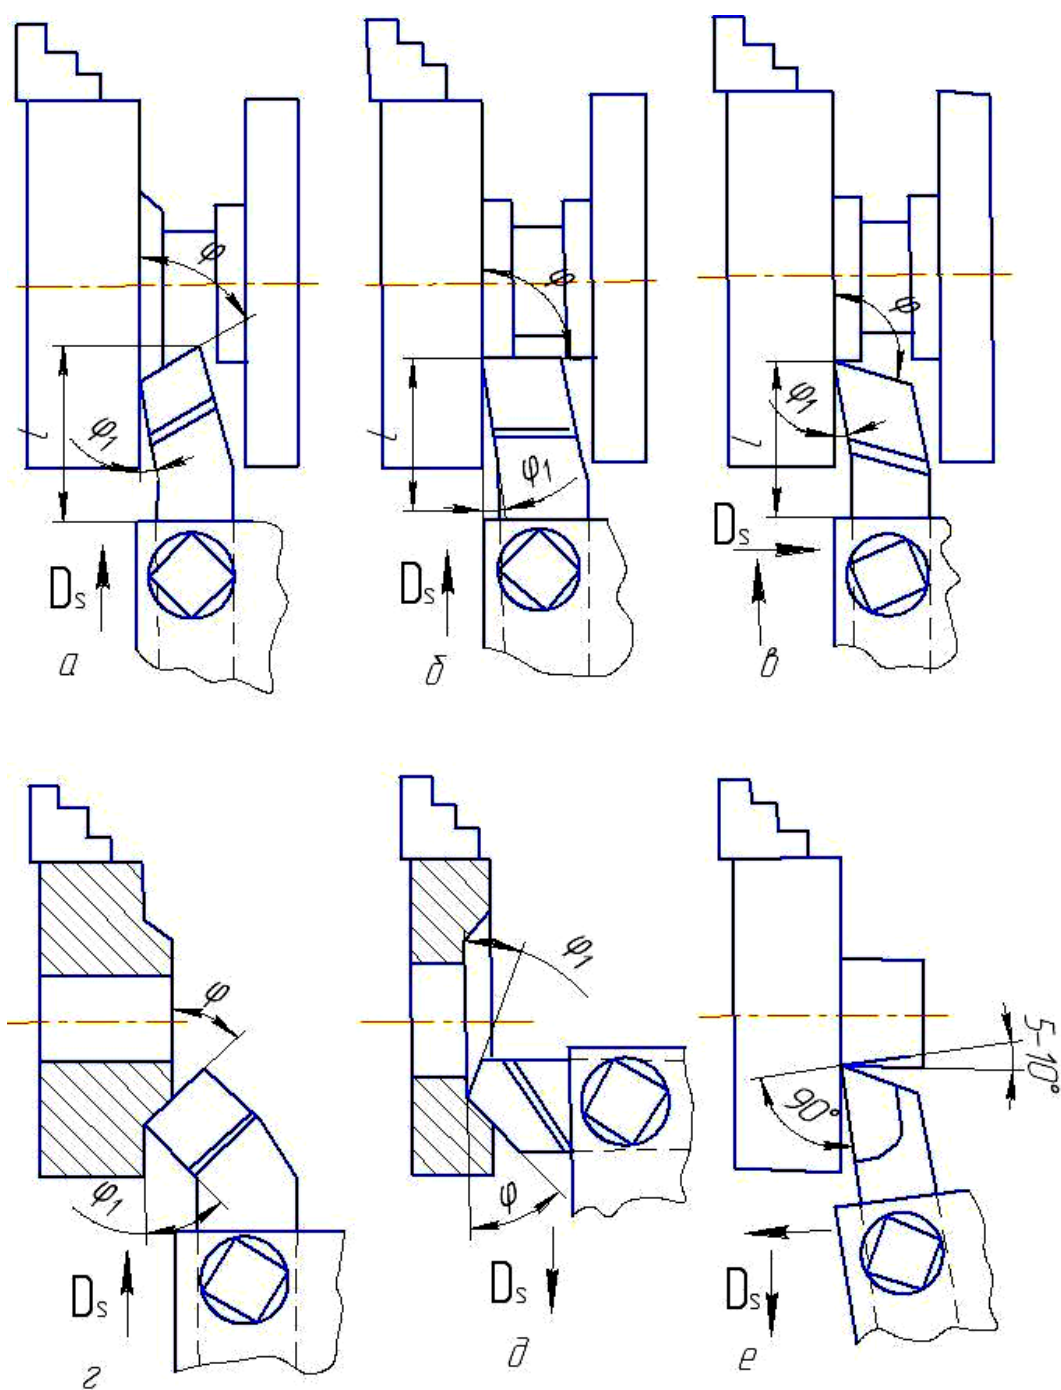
Резцы для обработки торцовых поверхностей:
